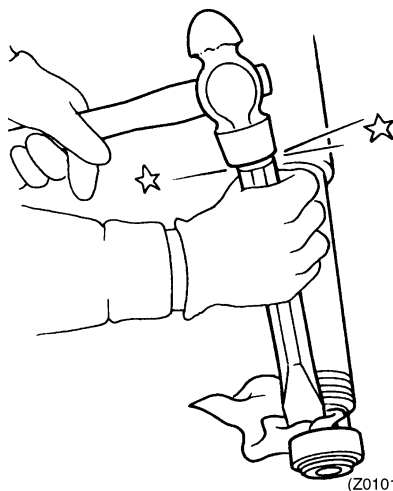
Снятие внутреннего кольца подшипника винтового вала
